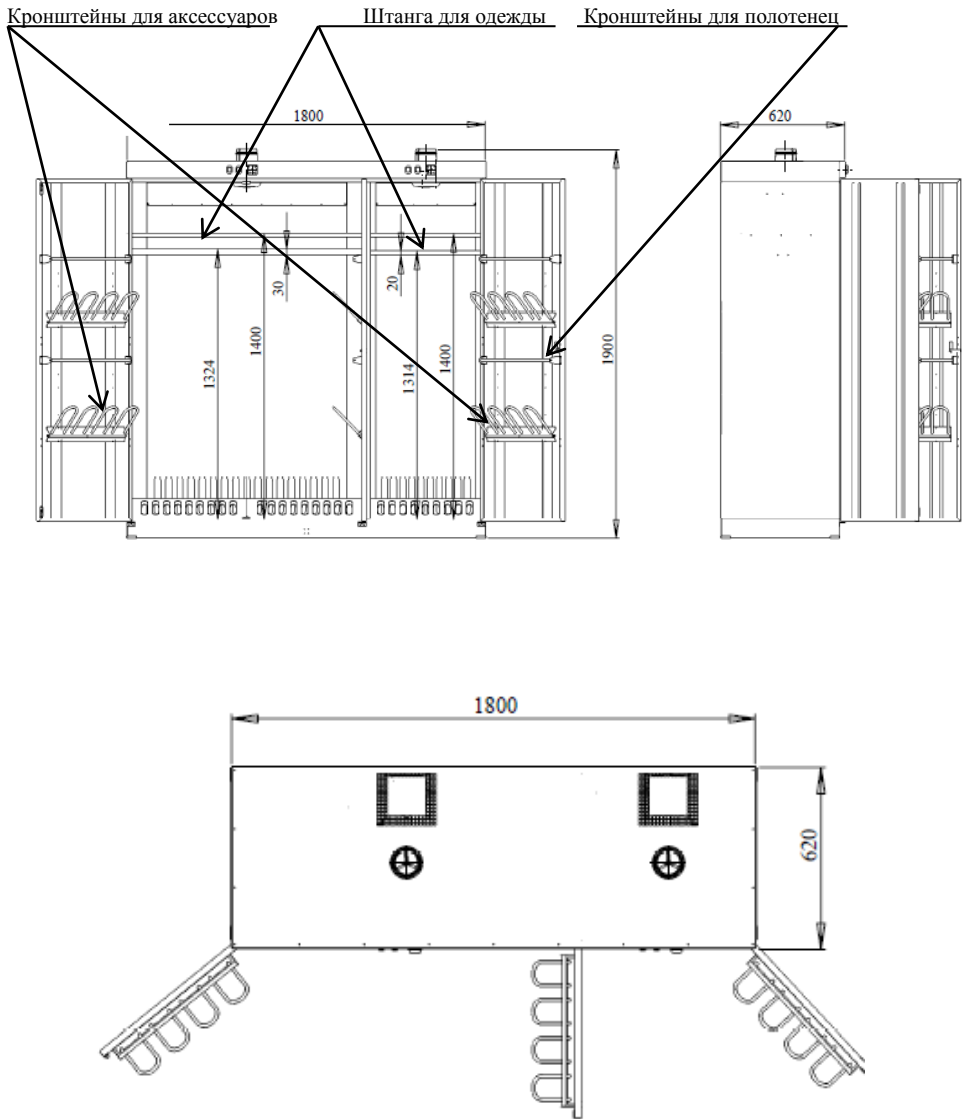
Внешний вид и габаритные размеры Шкафа Сушильного ШС – 8 Ш .
